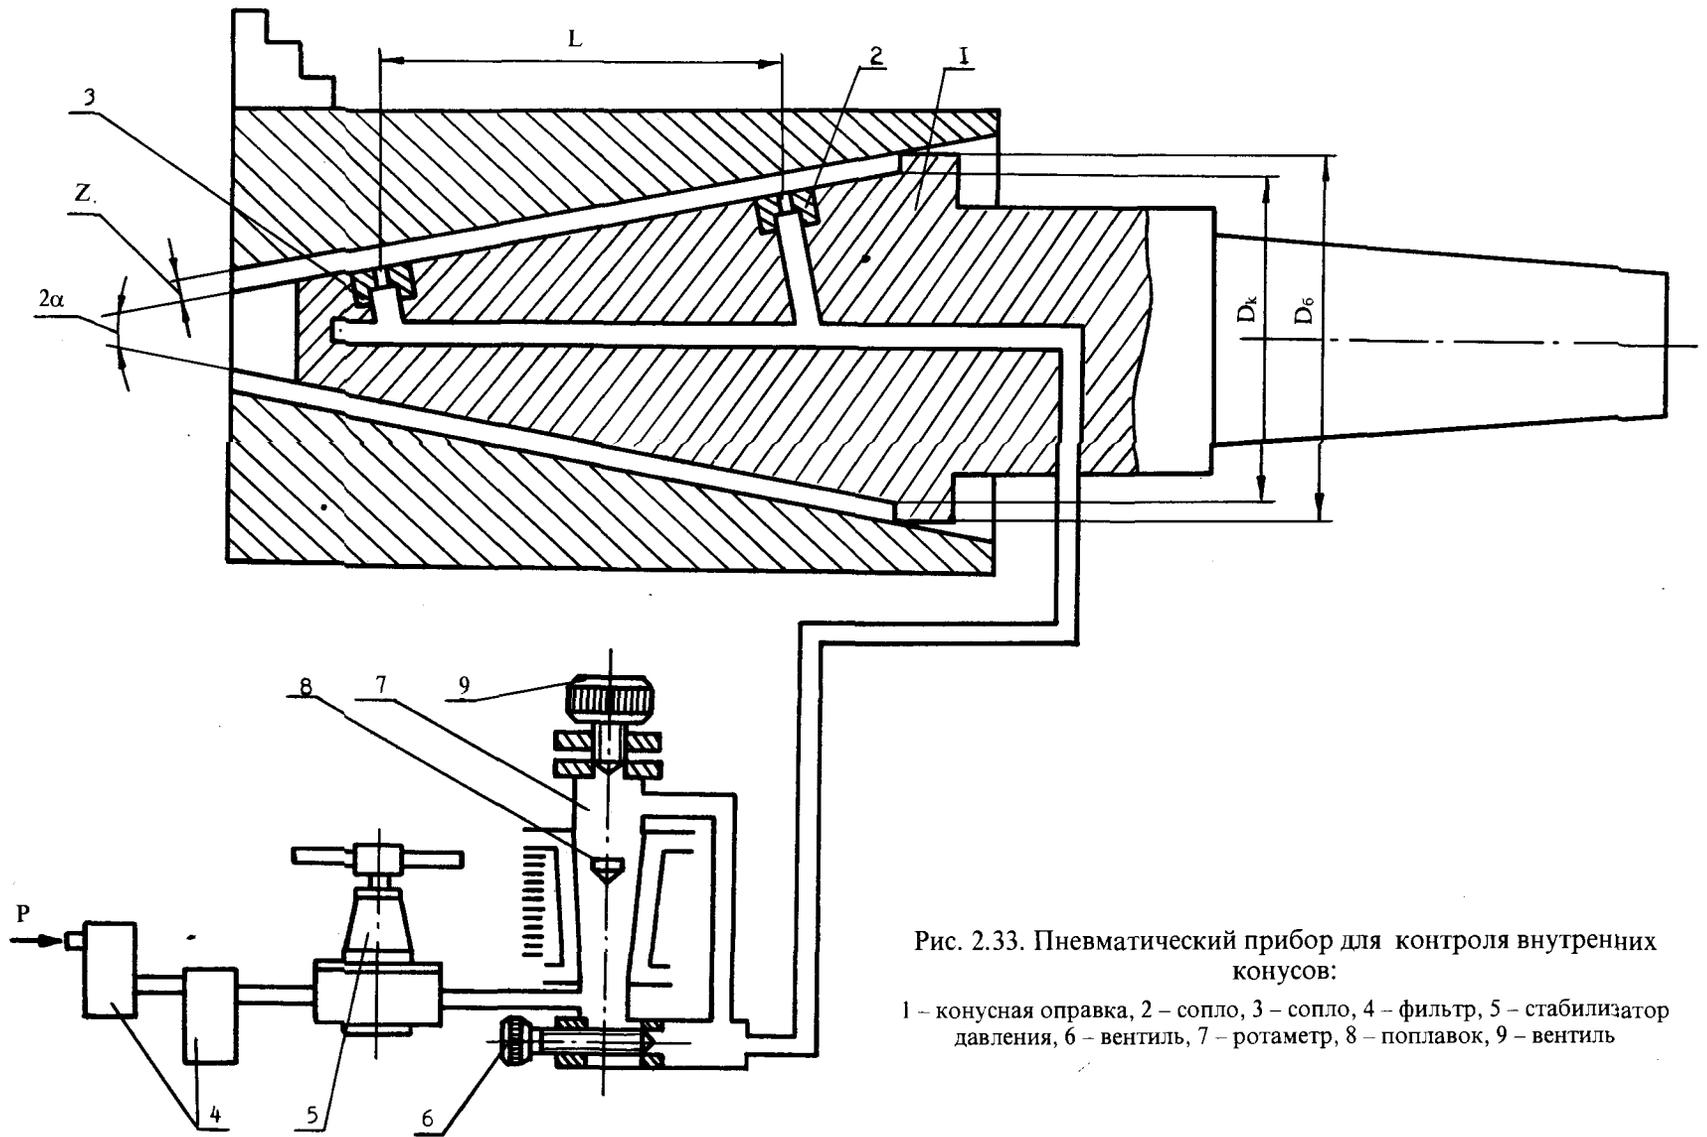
Пневматический прибор для контроля внутренних конусов:
